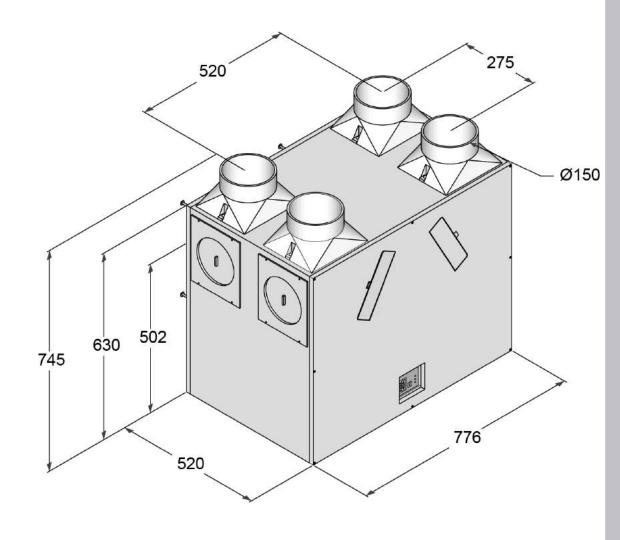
MCS 400; Abmessungen Maßangaben in Millimeter
